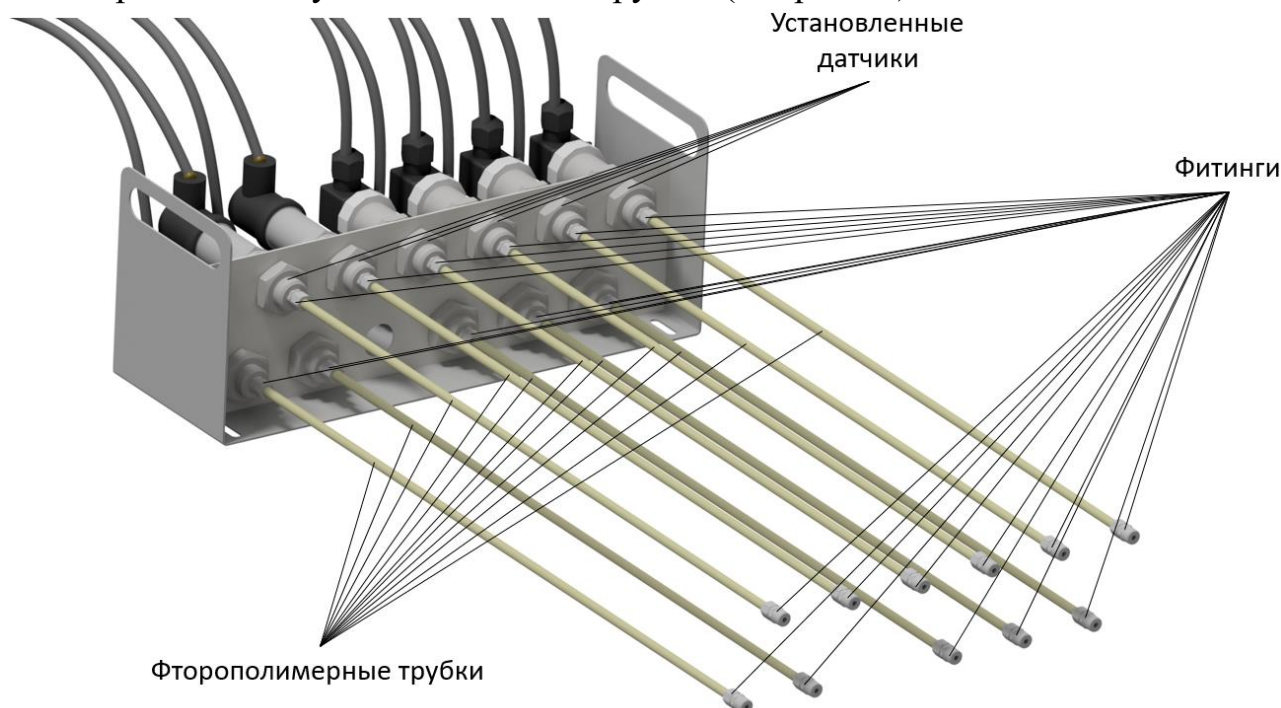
Установка фторополимерных трубок и фитингов датчиков давления
